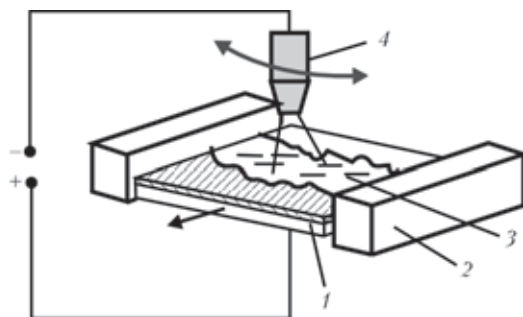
Схема работы плазменно-дуговой установки ОБ-1957: 1 — обрабатываемая заготовка; 2 — кристаллизатор; 3 — ванна жидкого металла; 4 — плазматрон
